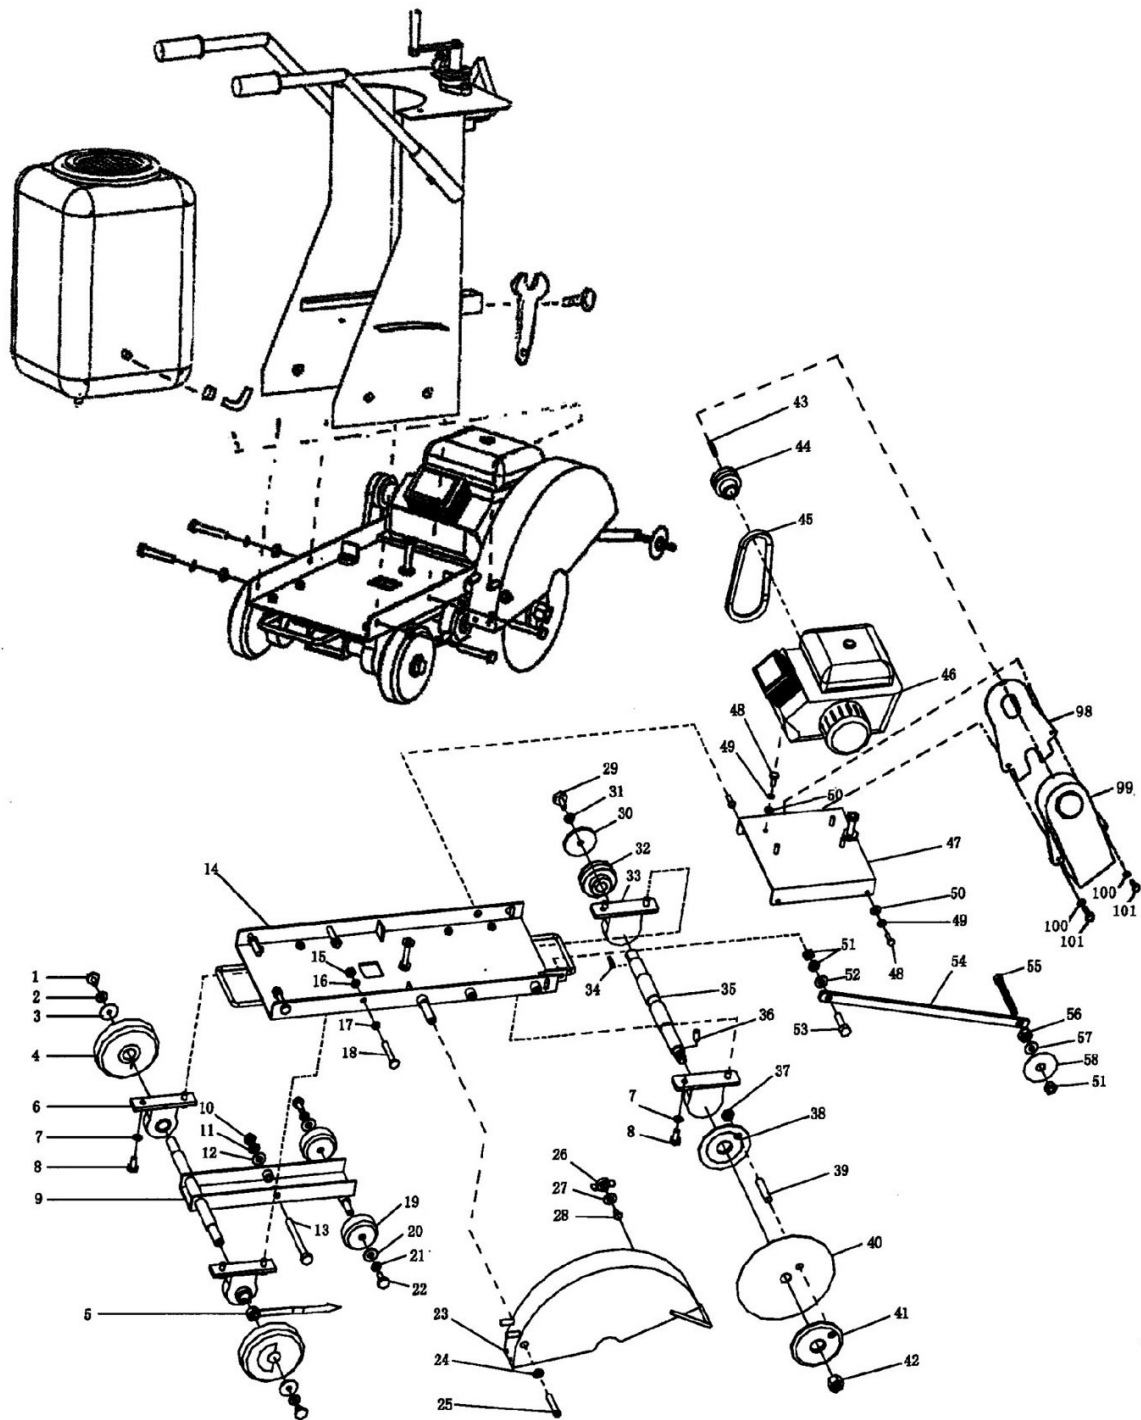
Despiece: bastidor, transmisión y grupo de corte
